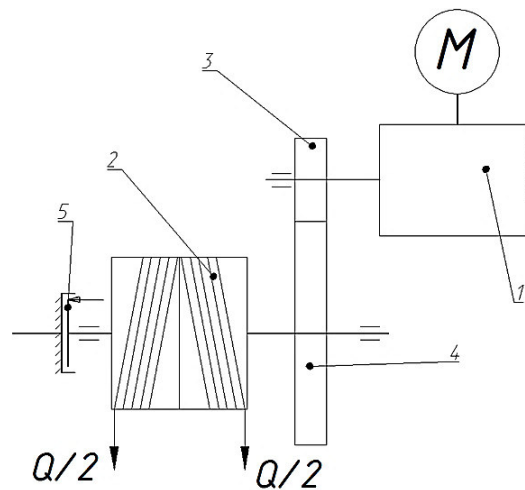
Кинематическая схема привода подъема телекамеры модернизированной ТВШ: 1 – цилиндро-червячный мотор-редуктор; 2 – барабан; 3 – шестерня; 4 – зубчатое колесо; 5 – тормозное устройство [Kinematic diagram of the lift drive for an upgraded TVSH: 1 - helical-worm gearmotor; 2 - drum; 3 - gear; 4 - gear wheel; 5 - braking device]
